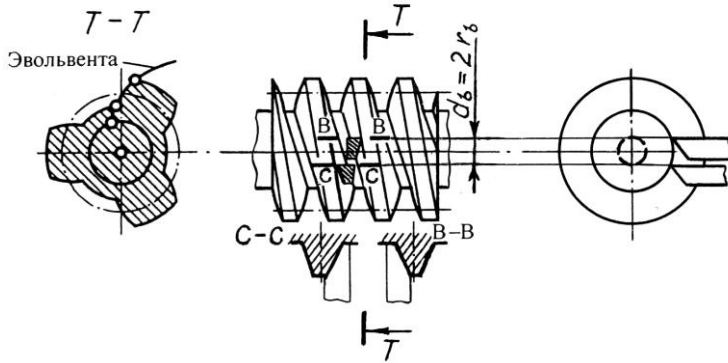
Эвольвентный червяк ZJ и схема установки резцов для нарезания витков правого направления
